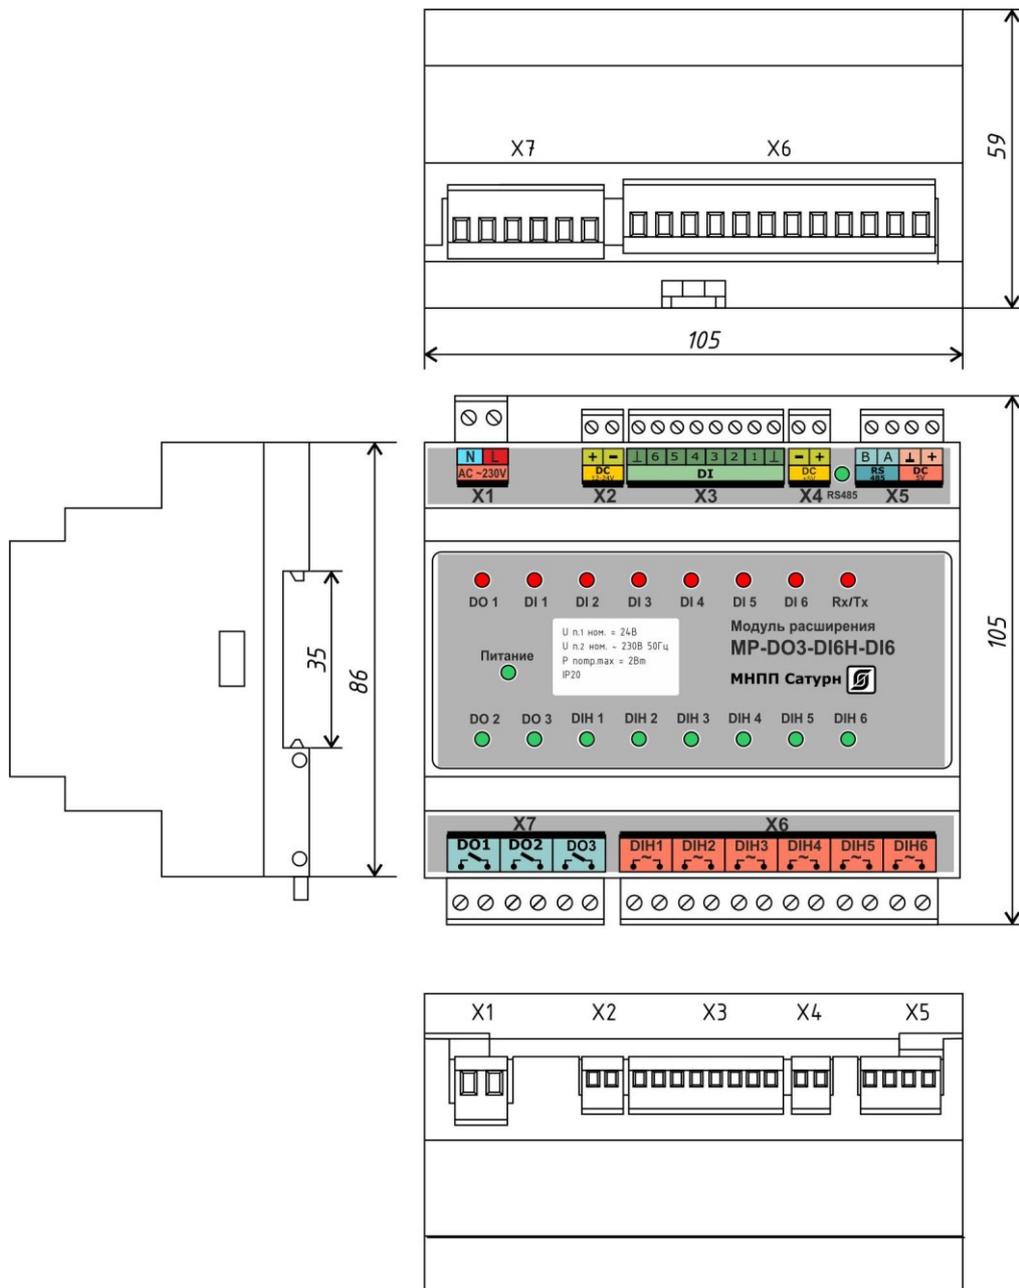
Габаритные размеры модуля расширения MP-DO3-DI6H-DI6
